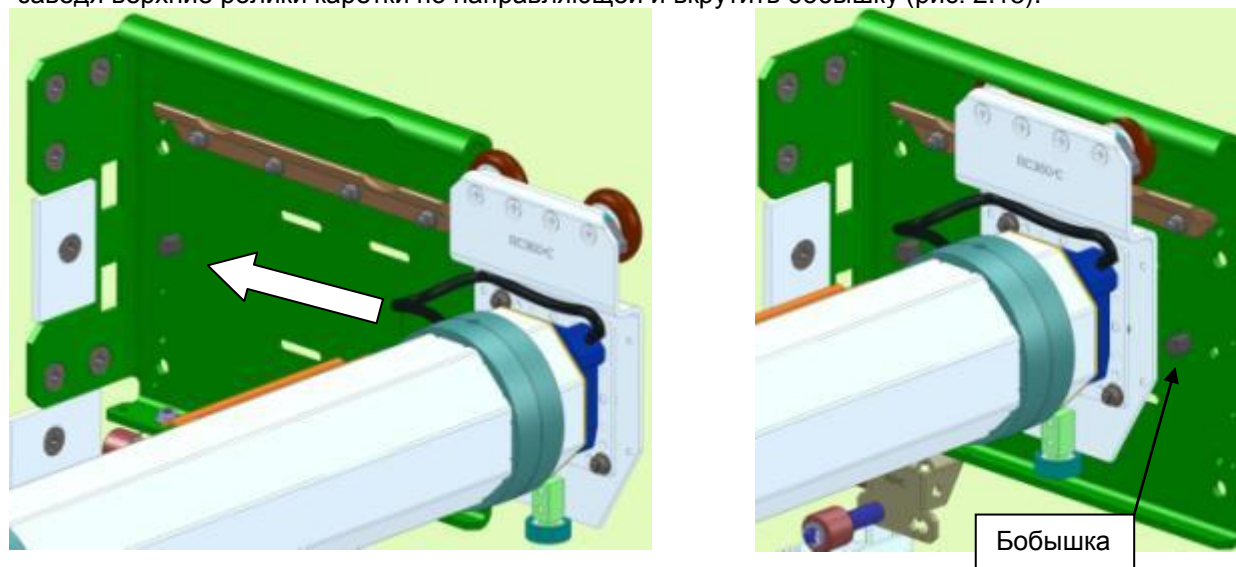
Установка каретки RC360/С с приводом на консоль ССМ
